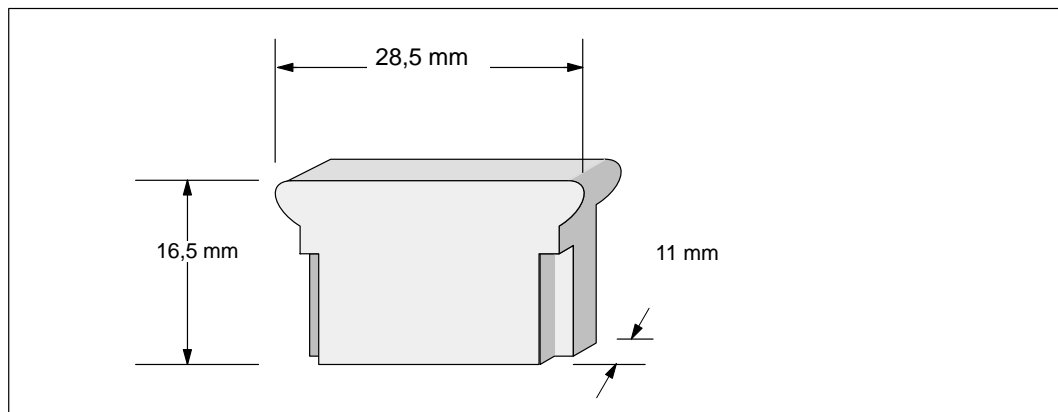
Dimensioni del modulo di batteria - 16K x 8
